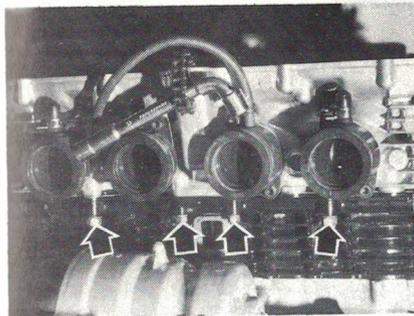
Fixations sous l'arrière de la culasse (Photo RMT)
